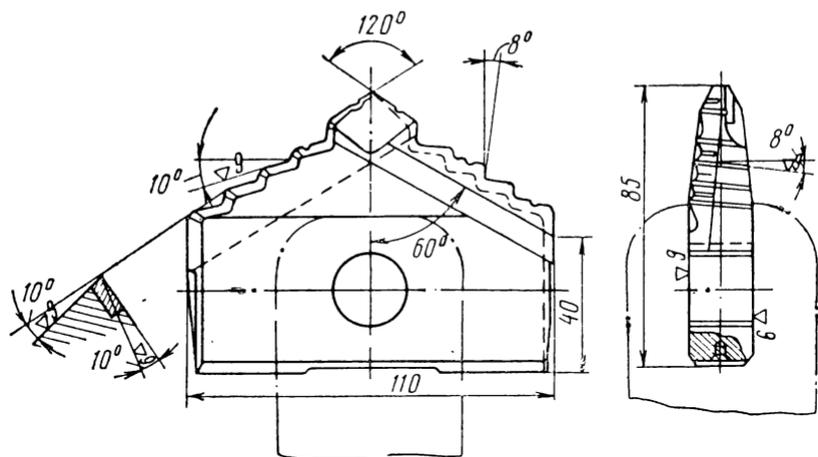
Ступенчатое перовое сверло для глубокого сверления
